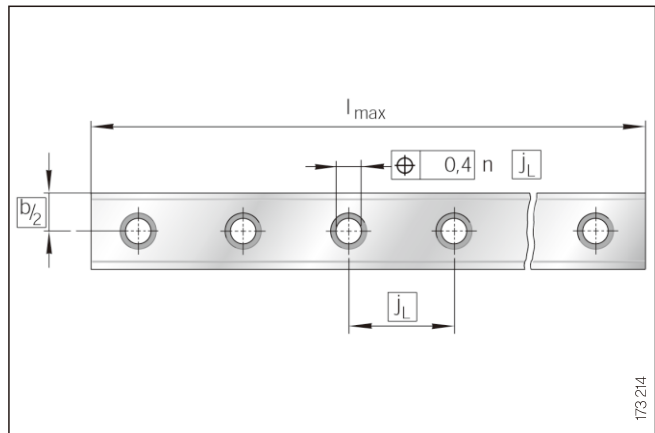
가이드웨이의 위치 및 길이 공차 - DIN ISO 1101에 의거하는 구멍 패턴
